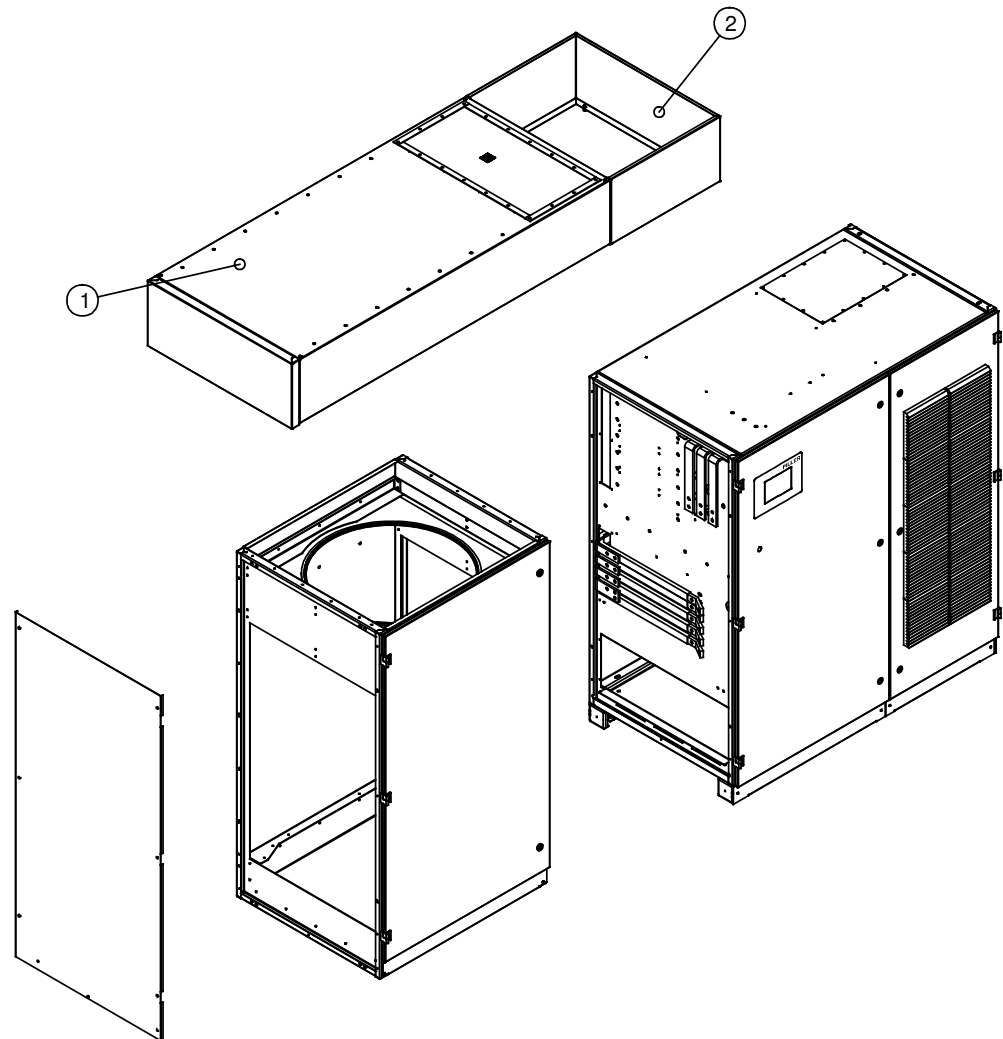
Einzelteile UB420 – UB625 Schalldämpfer
